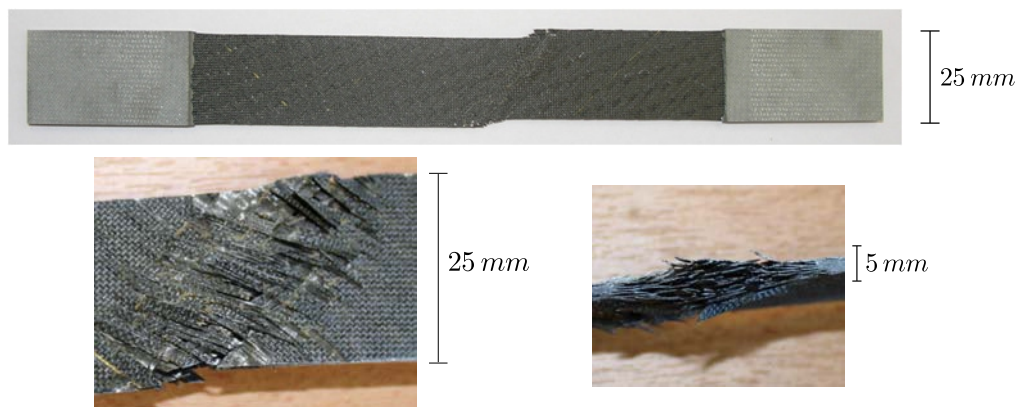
Faciès de rupture des éprouvettes de type B
